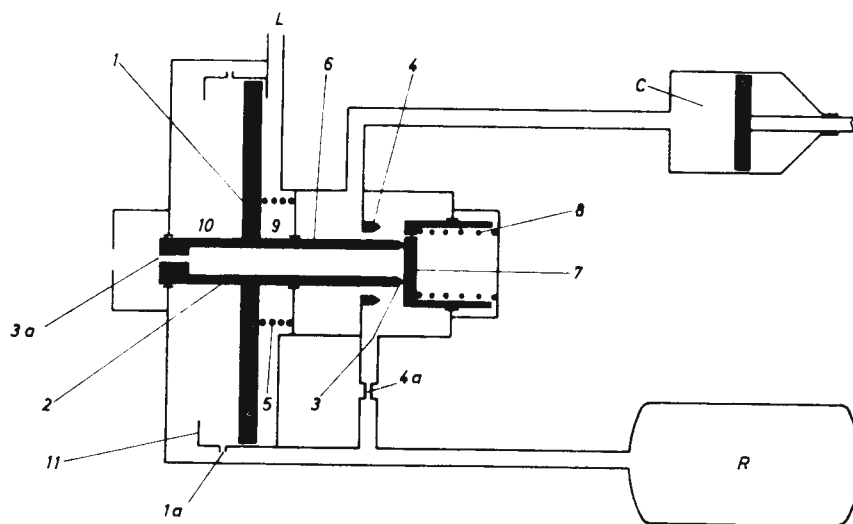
Styreventil, type Fe 115. Bremsstilling.
